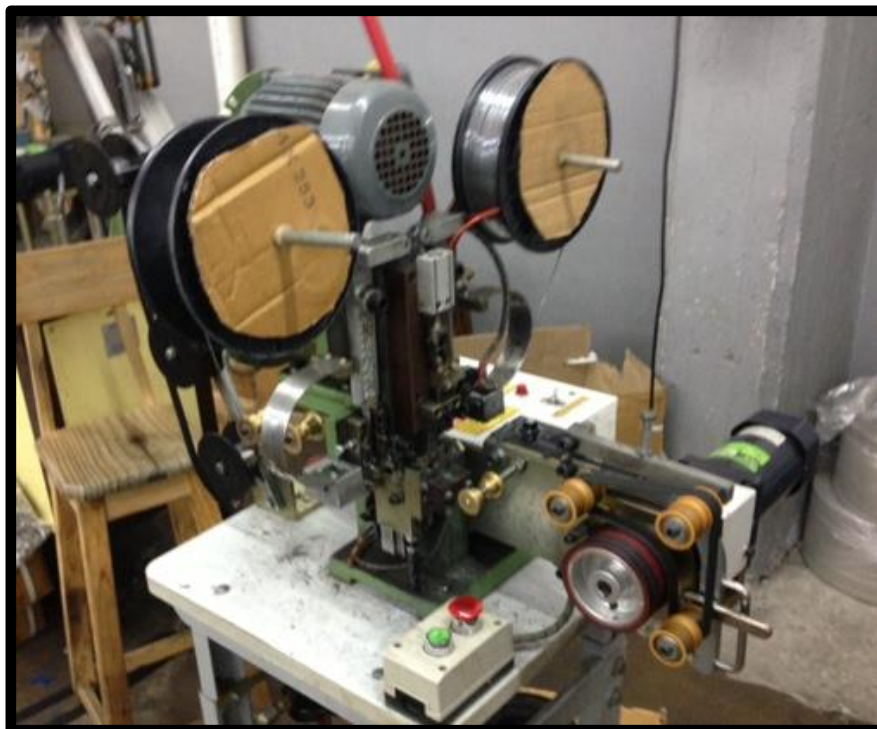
Máquina colocadora de topes superiores (Auto Double Top Stop M/C SE-125-
